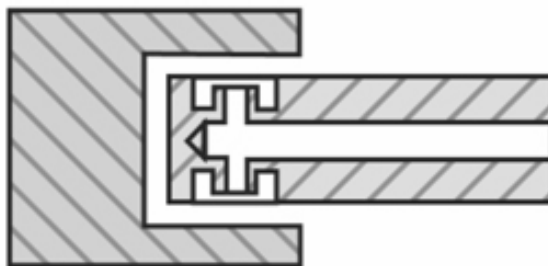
Вимірювання розміру заглиблення заготовки
